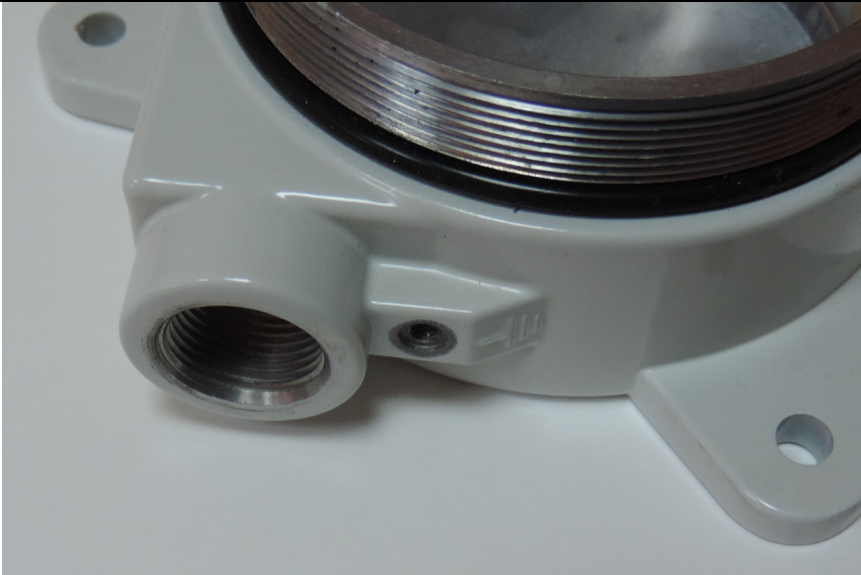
Монтируемый корпус прибора с патрубком (резьба М20х1,5)
